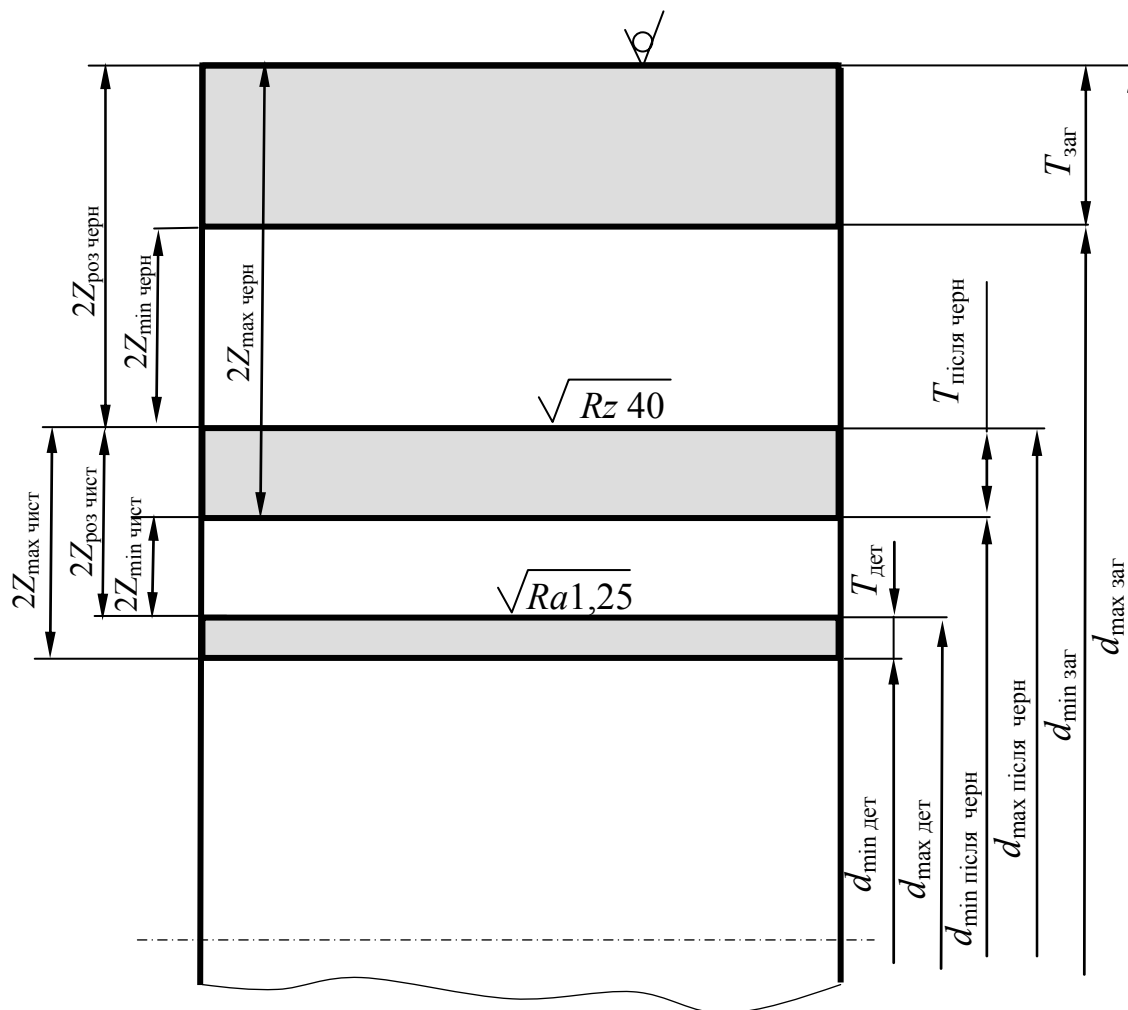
Схема розташування припусків і допусків деталі при токарській обробці
